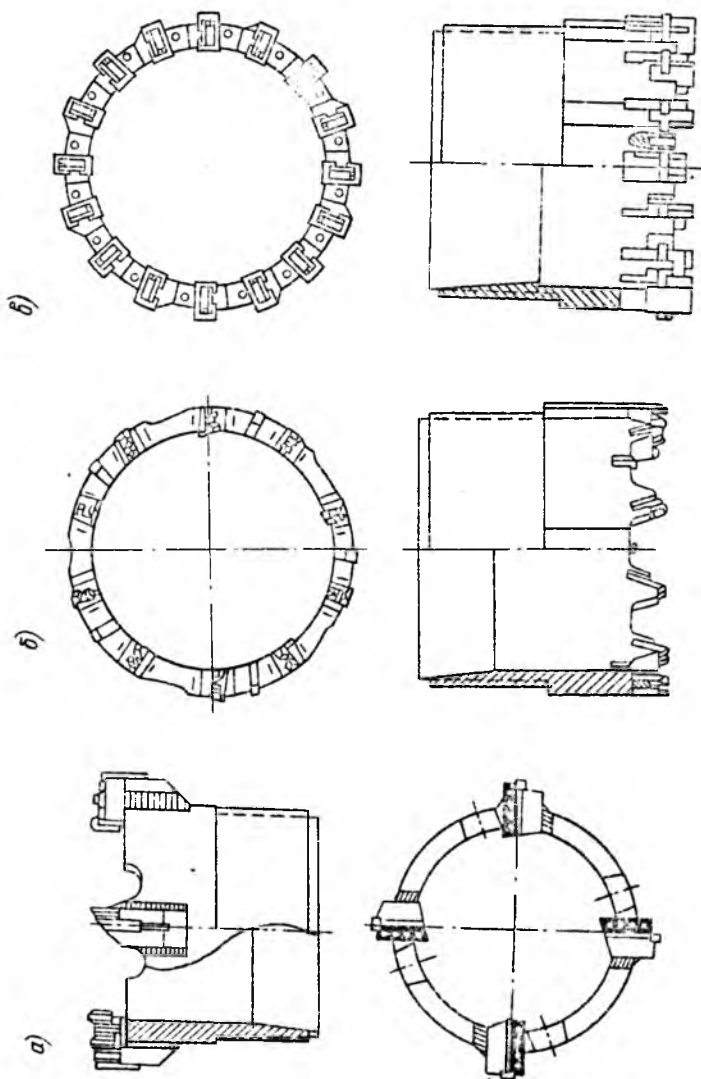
Твердосплавные коронки: а - ребристая; б - резцовая; в - самозатачивающаяся
